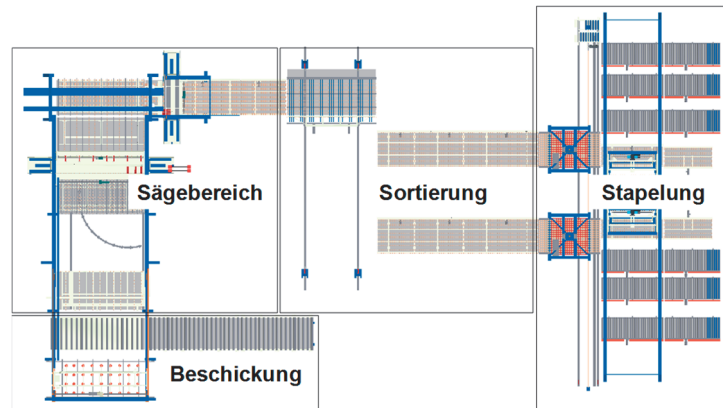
Klassisches Layout einer Plattenaufteilanlage
